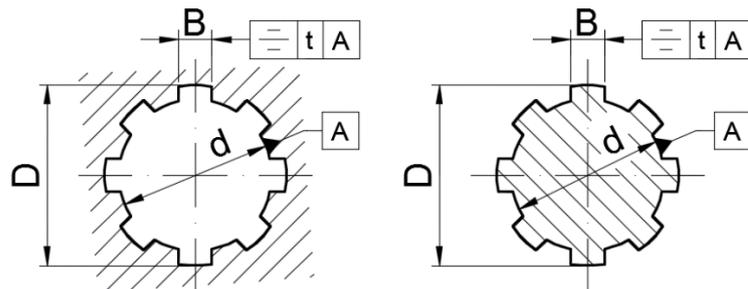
Tolerancias dimensionales y geométricas a designar en un conjunto (árbol-cubo) estriado.
